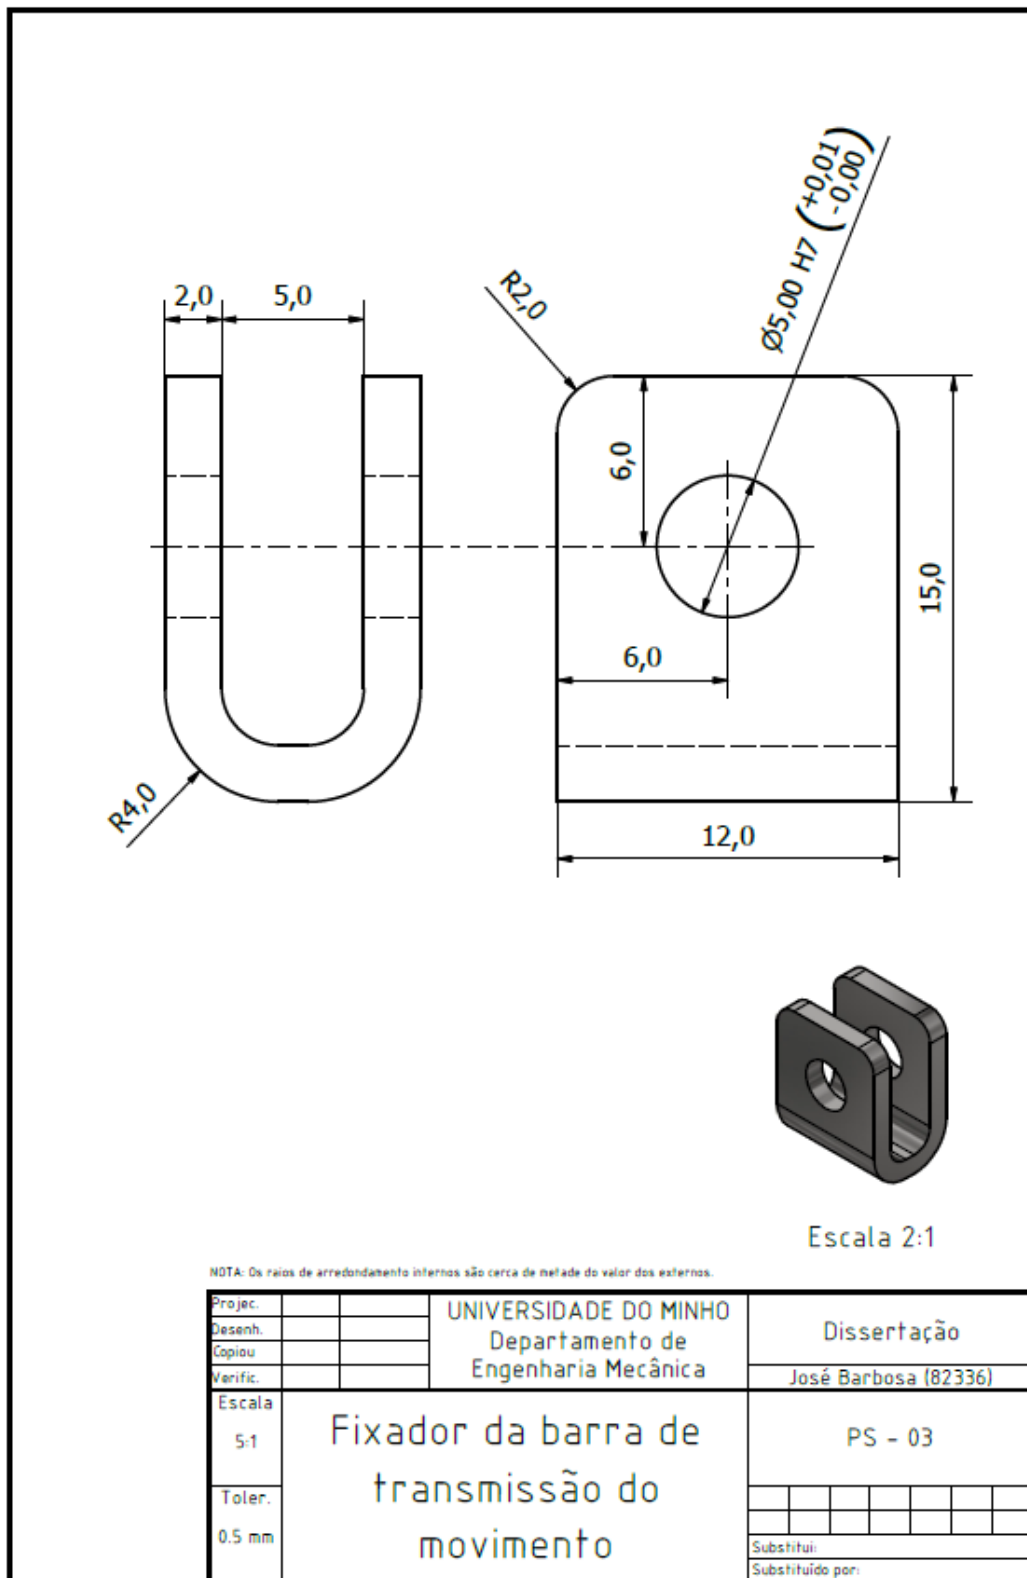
Figura Anexo III-28 – Desenho técnico do fixador da barra de transmissão do movimento.
